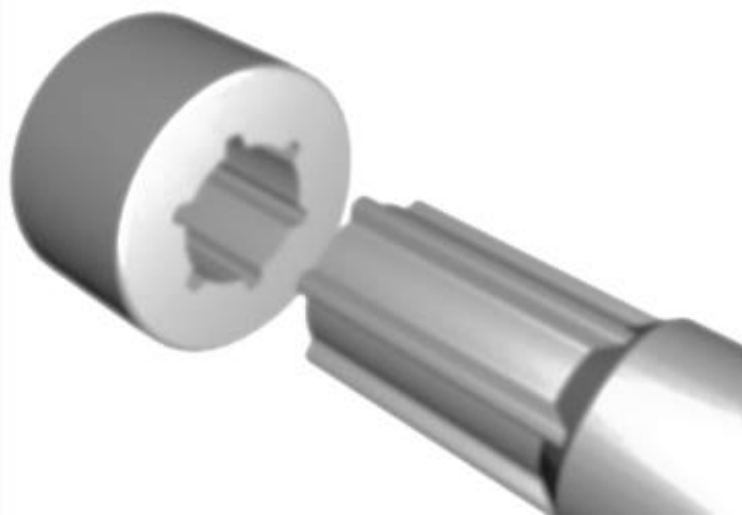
Образец зубчатого (шлицевое) соединение.
